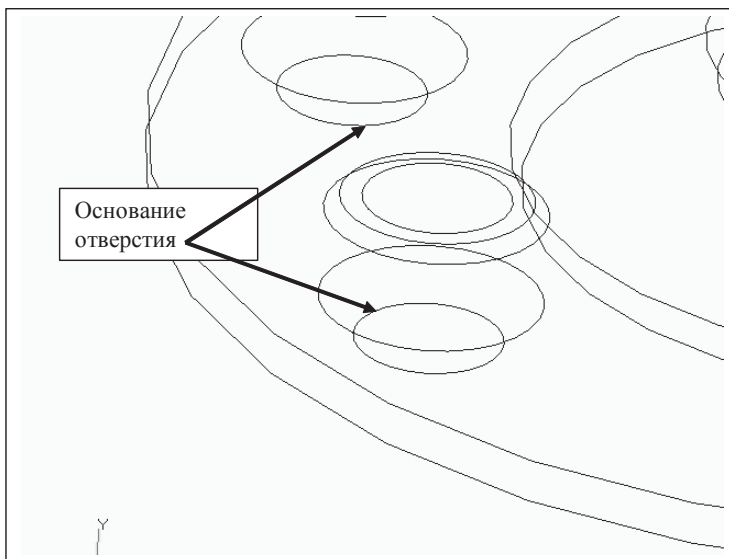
Общий вид зоны конструкции детали для приложения закрепления
